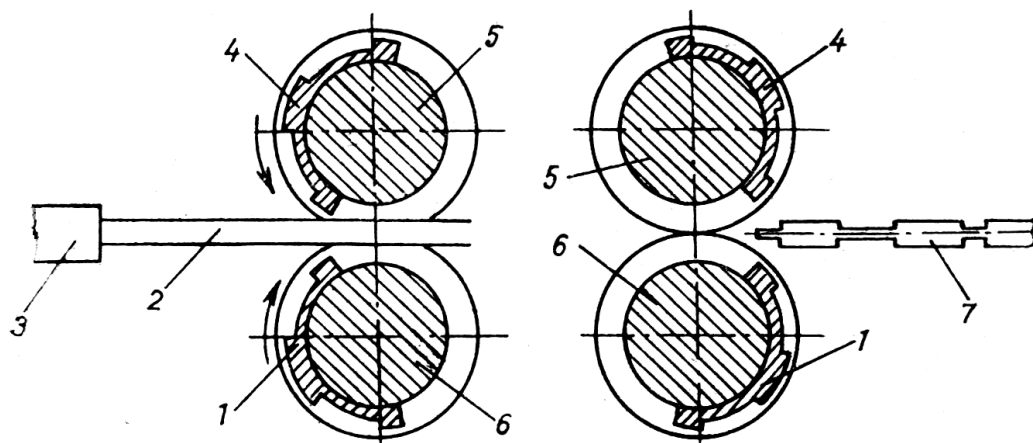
Початкова (а) та кінцева (б) стадії вальцювання: 1, 4 — половинки секторного штампа; 2 — вихідна заготовка; 3 — упор; 5, 6 — вальці; 7 — кованка
